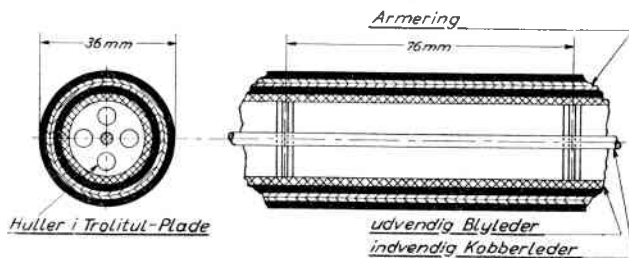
Modtagerantennenkabel, Type A.S.26.
